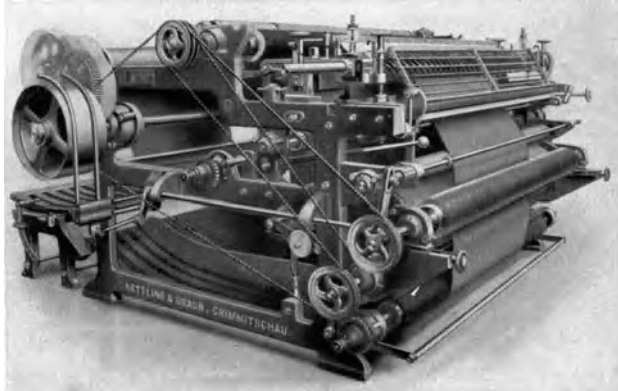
Schermaschine mit einem Schneidzeug. (Kettling & Braun, Crimmitschau.)
